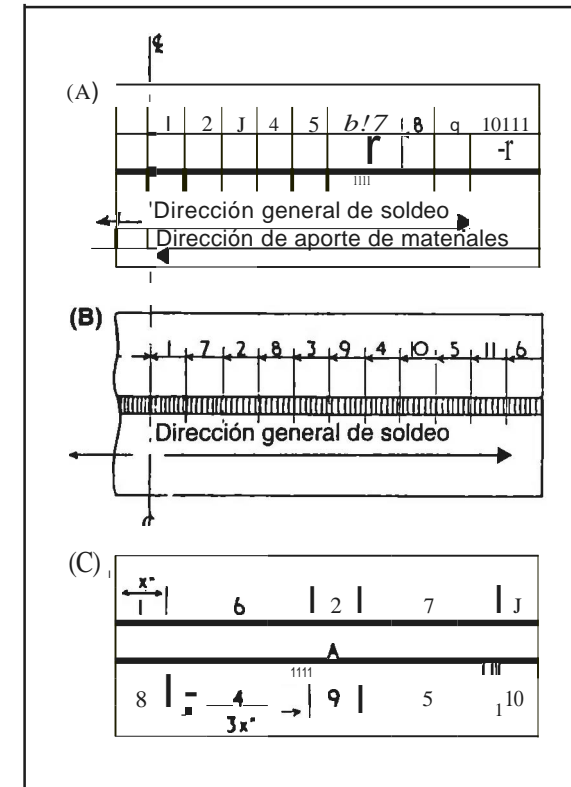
(A) SOLDEO DE PASO DE PEREGRINO. (B) SOLDEO A SALTOS. (C) TÉCNICA PARA REALIZAR DOS SOLDADURAS EN ÁNGULO EN FORMA DE T
